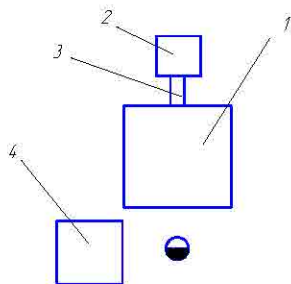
9 - Організація робочого місця штампувальника для холодної правки: 1- гвинтовий прес; 2-тара для поковок; 3-склиз;
